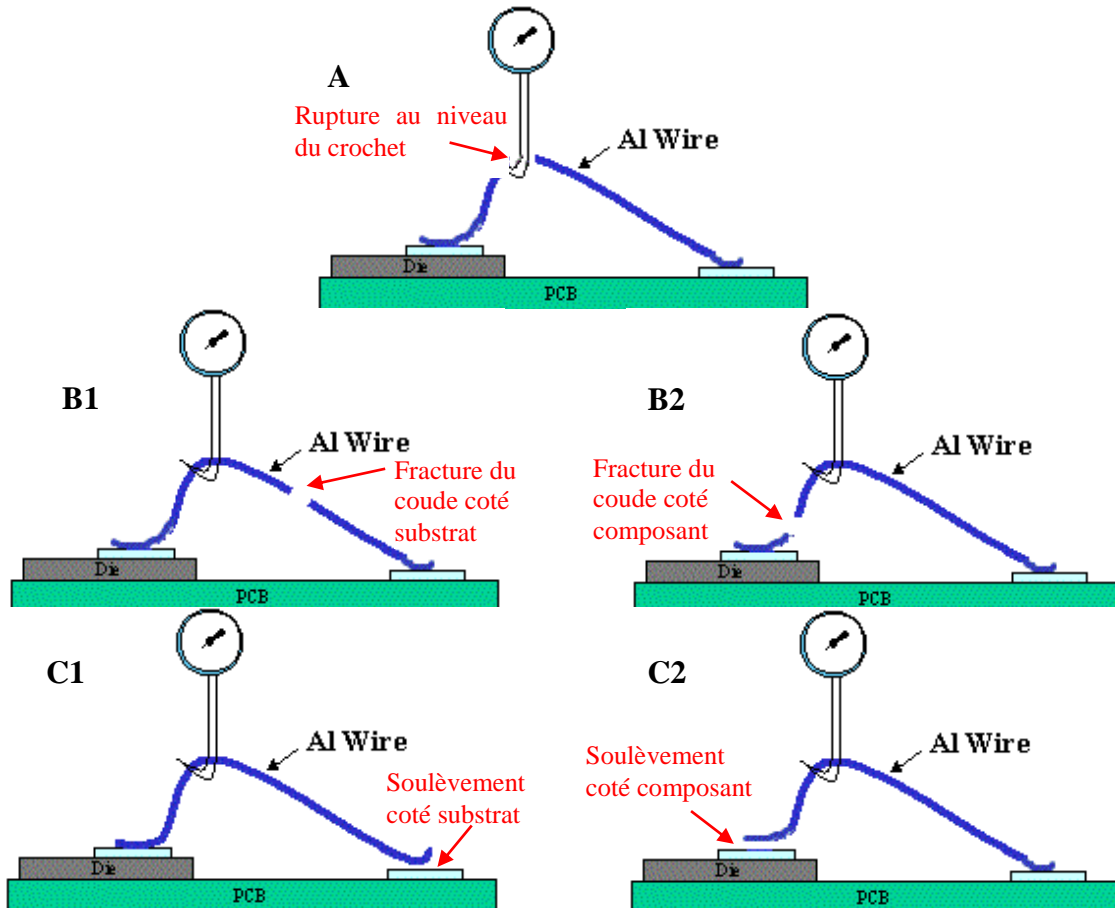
Les cinq principales zones de rupture du fil de câblage lors de l'essai d'arrachement
